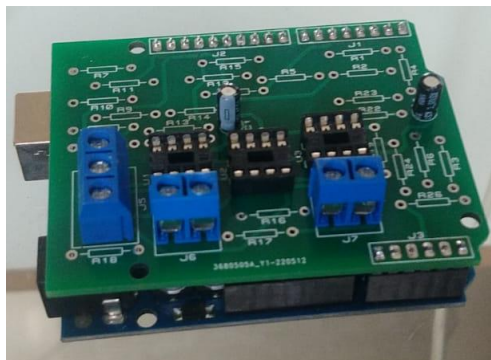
Diseño PCB integral ya en físico (primer diseño)
